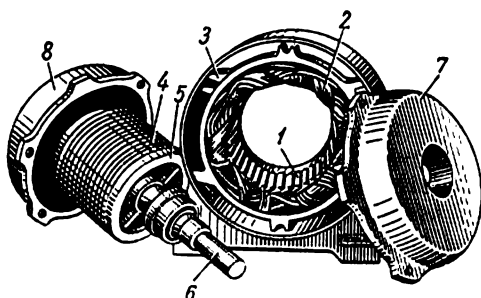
Moteur asynchrone à rotor en court-circuit démonté
